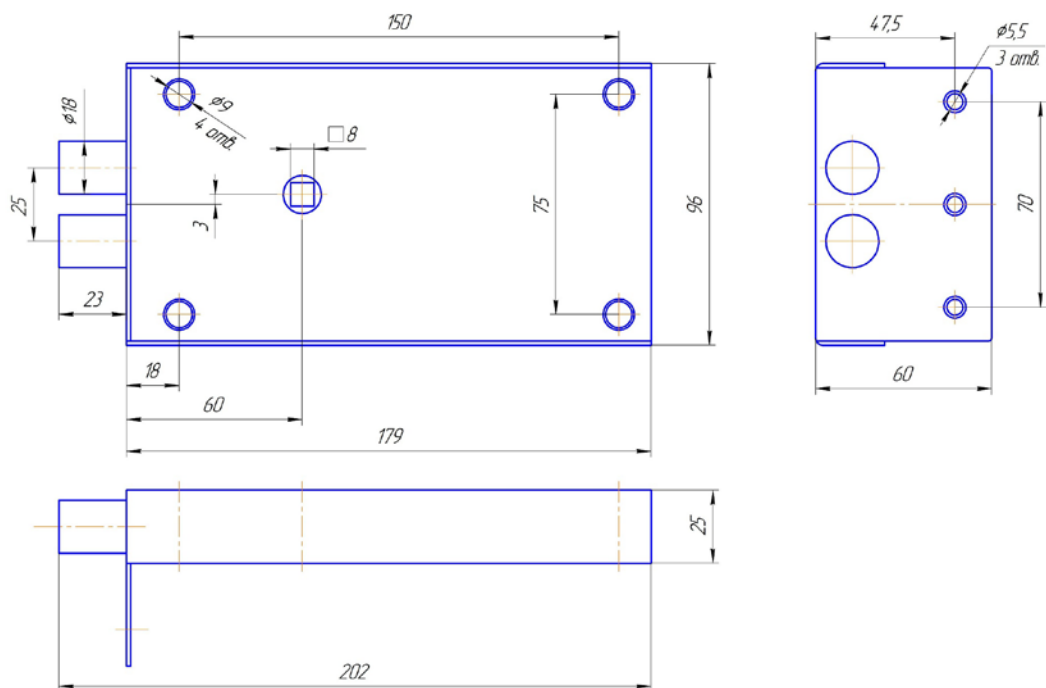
Установочные размеры накладного запорного устройства замка «Сюрприз-Герон»
